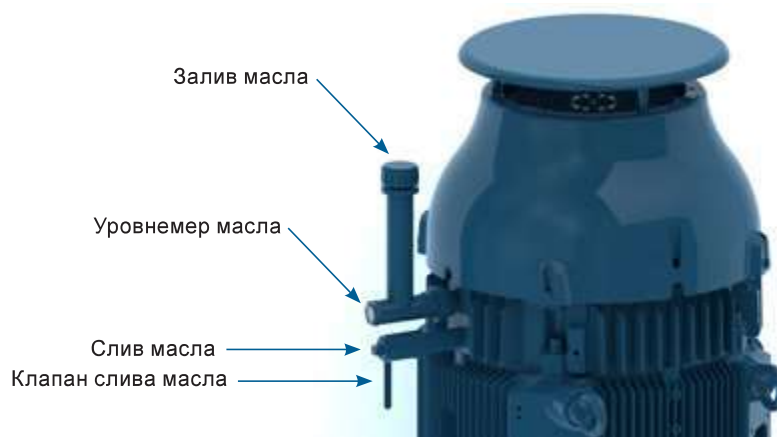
Подшипники со смазкой маслом - вертикальное исполнение
